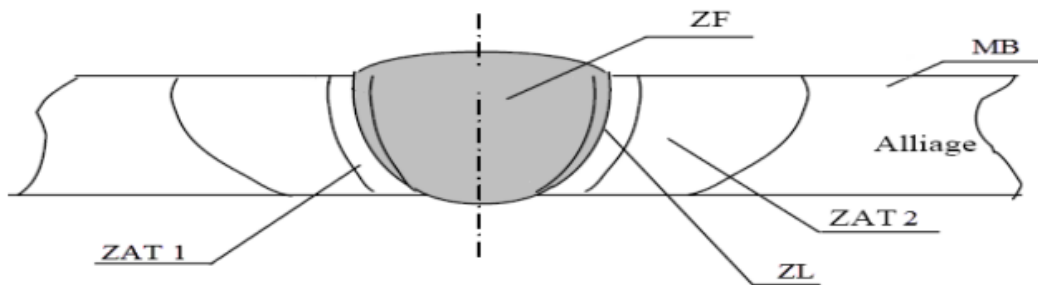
Zones caractéristiques lors du soudage du TA6V [22]
